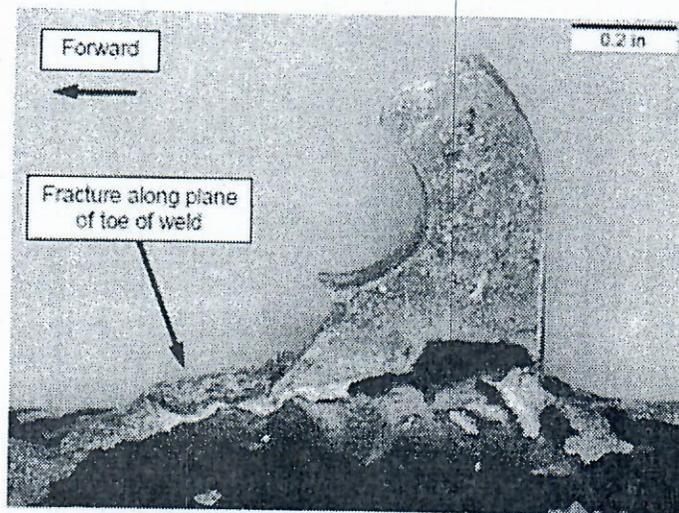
Vista cercana de la fractura de la oreja extremo delantero.
